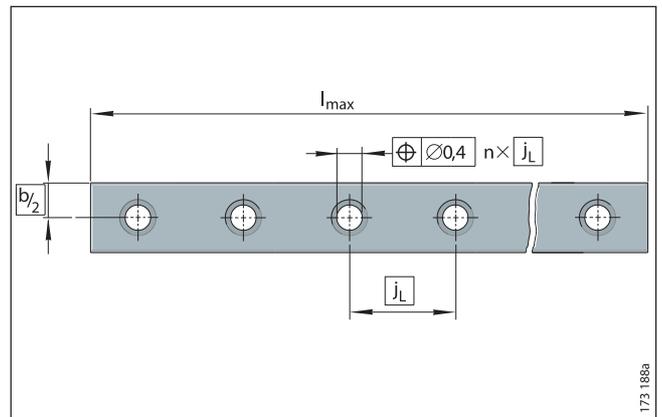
· Допуски расположения и длин для направляющих рельсов – отверстия в соответствии с DIN ISO 1101
